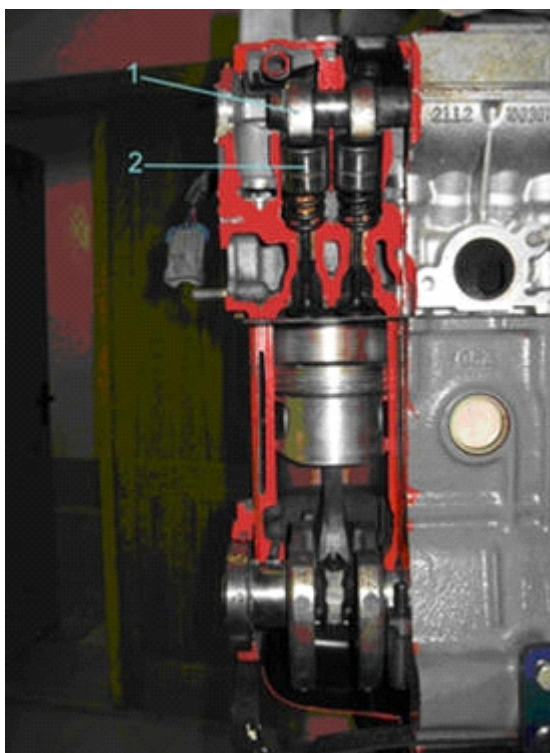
ГРМ двигателя ВАЗ-2112 с гидрокомпенсаторами:
